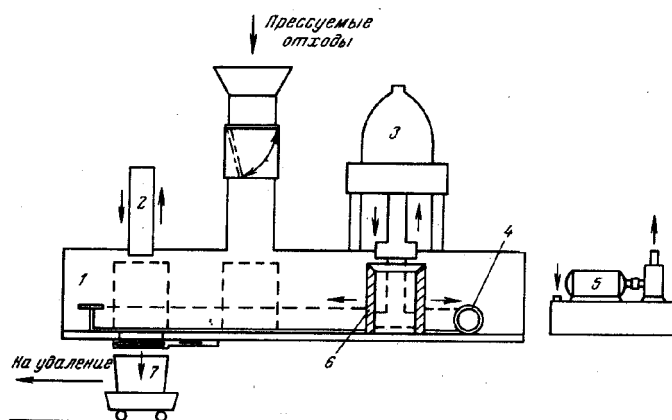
Схема установки прессования на базе вертикального гидравлического пресса (защитный бокс, гидротолкатель, пресс, привод пресс-формы, насосная станция, пресс-форма контейнер).
